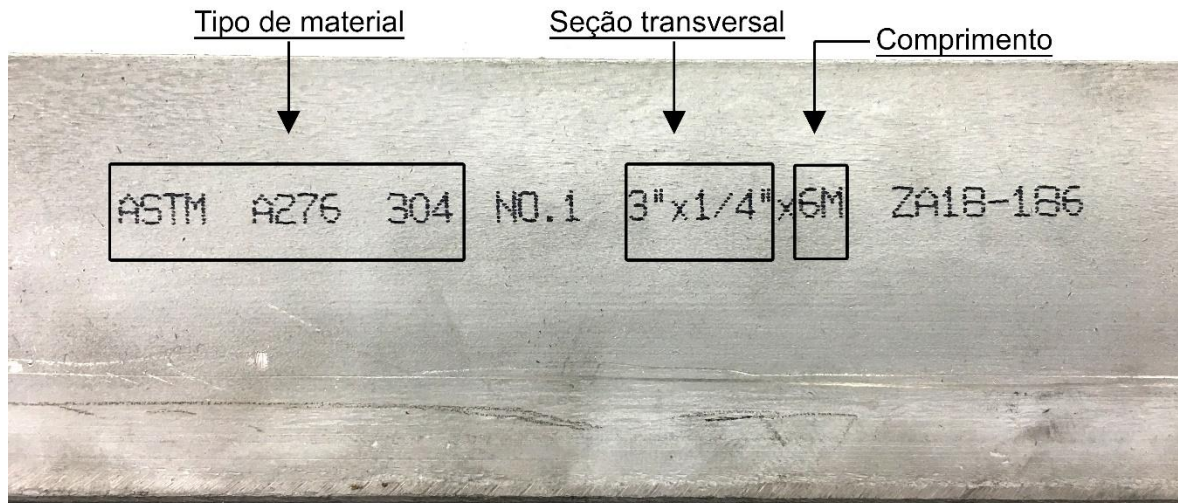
Especificação do material, dimensão da seção transversal e comprimento total do perfil
